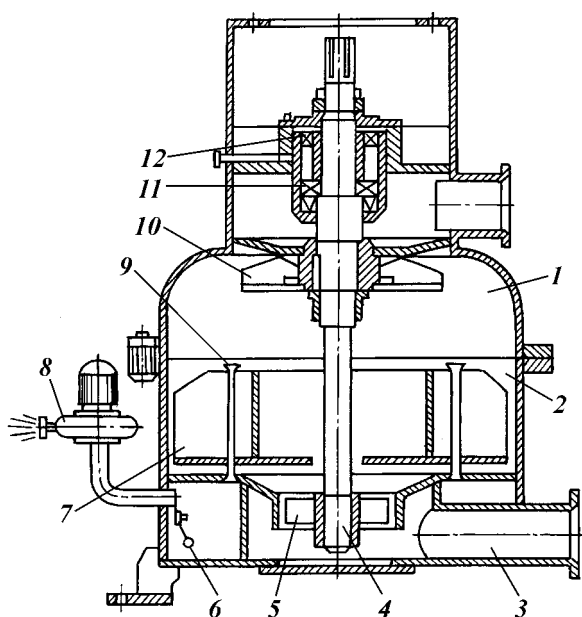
Центробежно-вакуумный дегазатор ЦВА:
